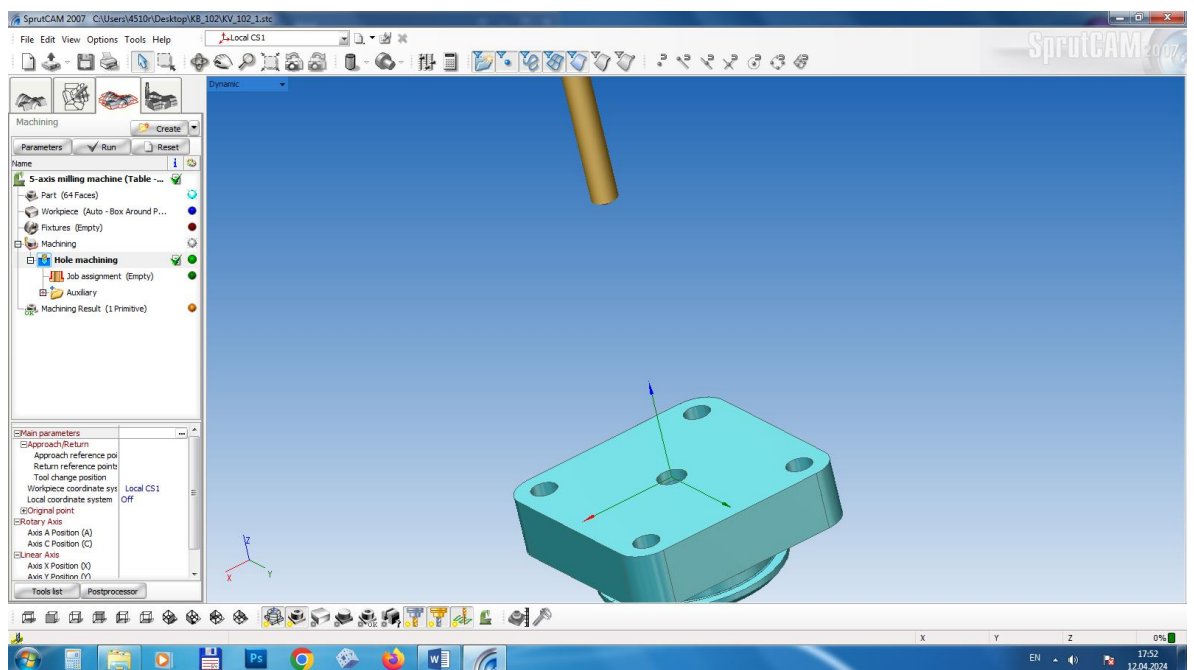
Інструмент і деталь після обробки на верстаті.
